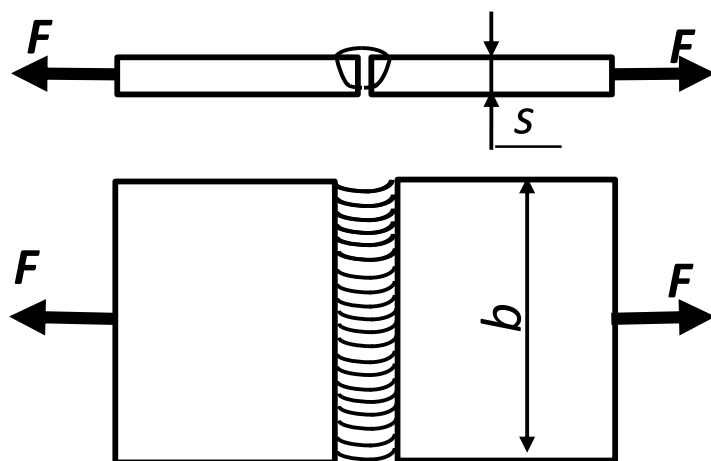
Расчет стыкового сварного шва на прочность
